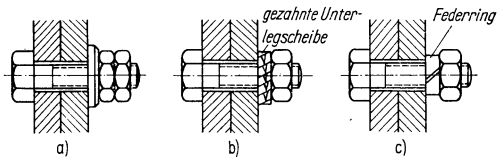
Schraubensicherung durch Gegenmutter (a), gezahnte Unterlegscheibe (b) und Federring (c)
